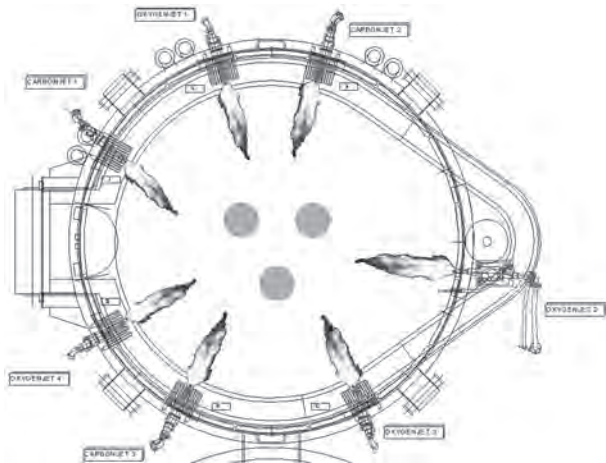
Схема расположения модулей «DANARC» в корпусе ДСП-100
